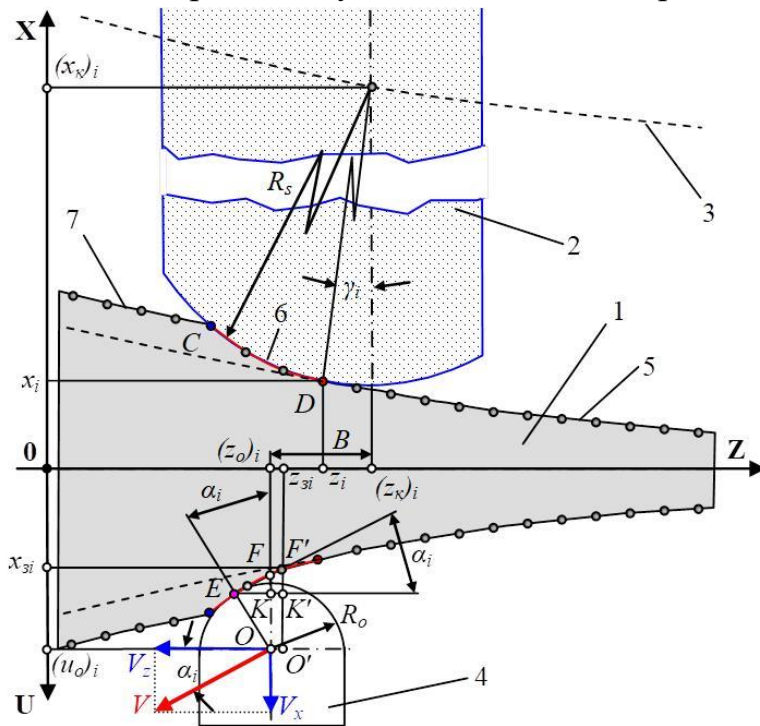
Схема формоутворення поверхні оправки при шліфуванні
